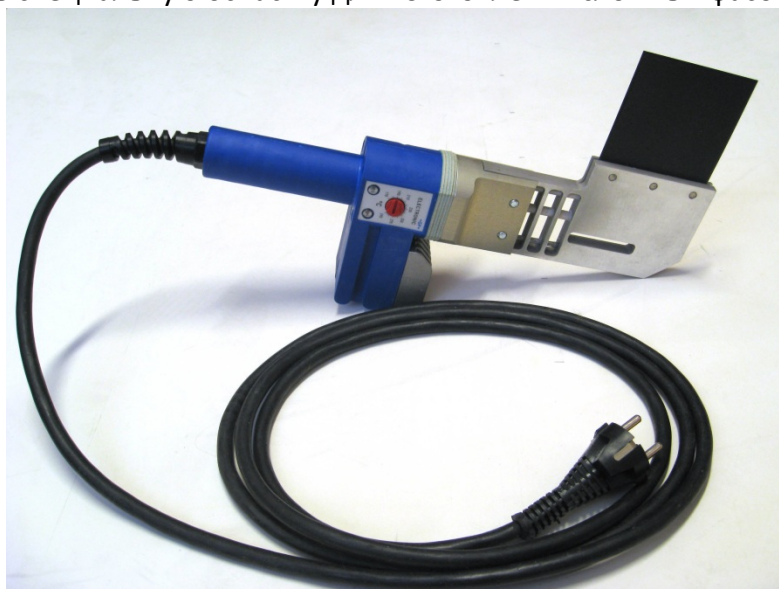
Аппарат для стыковой сварки модель Л-070.
